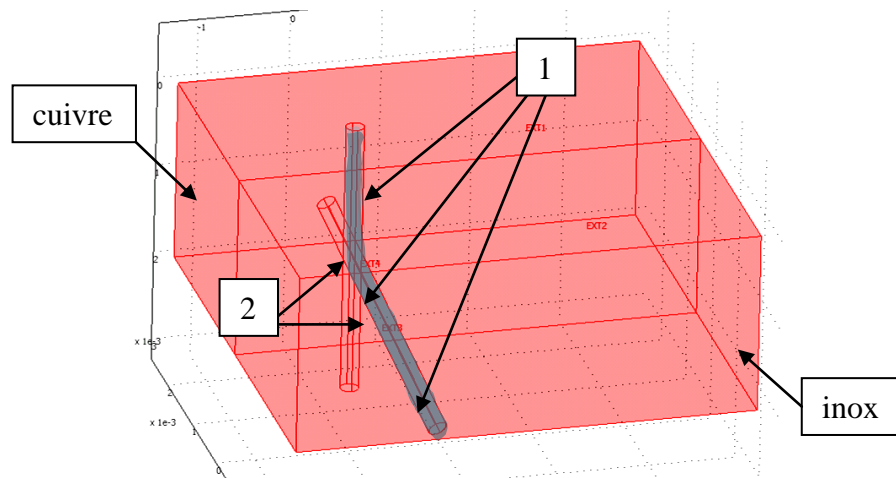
La géométrie du modèle 3D de soudage cuivre-AISI 316L par laser Nd:YAG.
